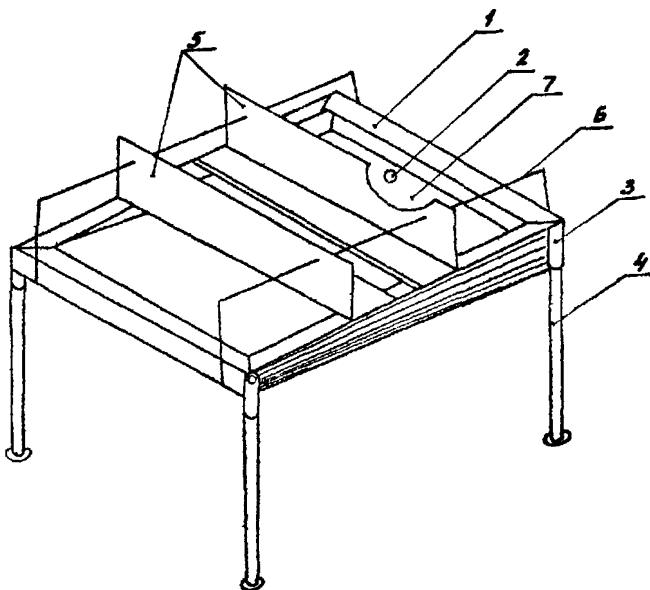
Приспособление для укладки деталей: 1 - каркас ;
